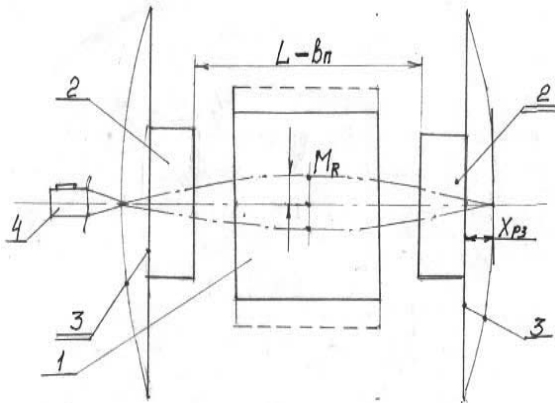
Прогиб вала: 1 – ротор, 2 – подшипник, 3 – подшипниковый щит, 4 – вал
